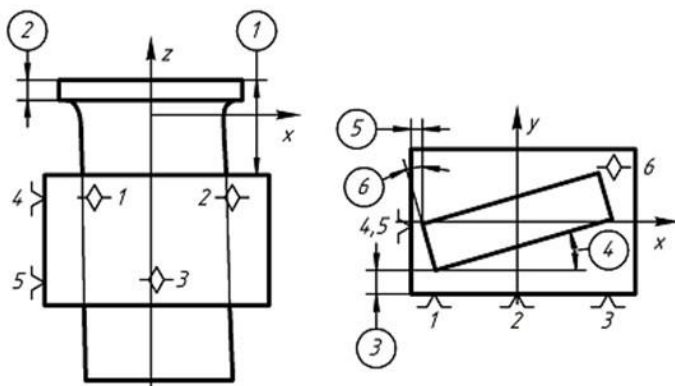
схема розташування установної й опорної баз під час обробки хвостовика лопатки компресора при її закріпленні в брикет (пристрій-супутник).
